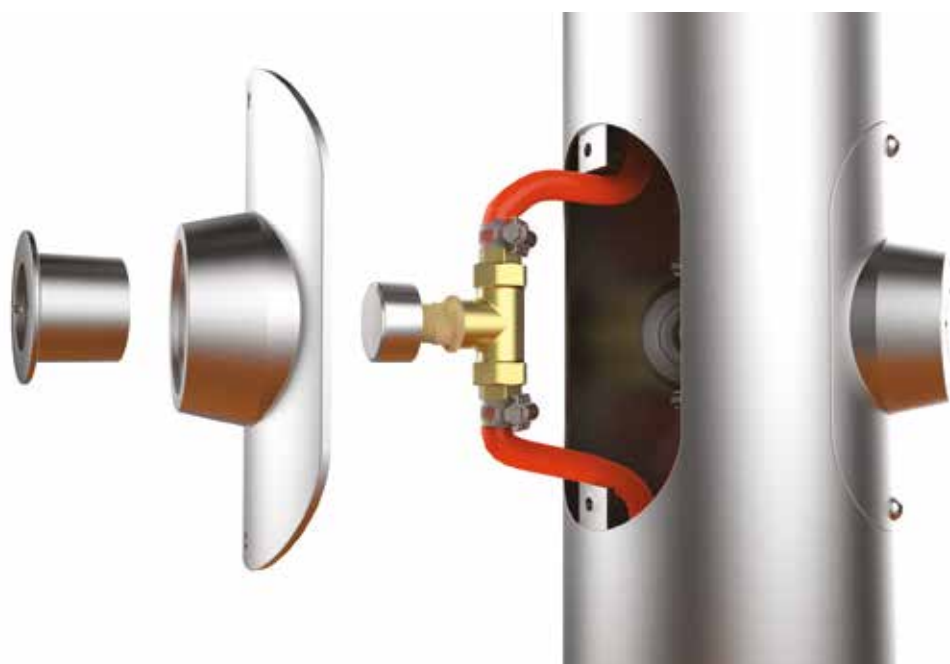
Canopla, Tampa Acesso Válvula e válvula Biopress Fabrimar. Vista explodida. Fonte: Elaboração própria.
